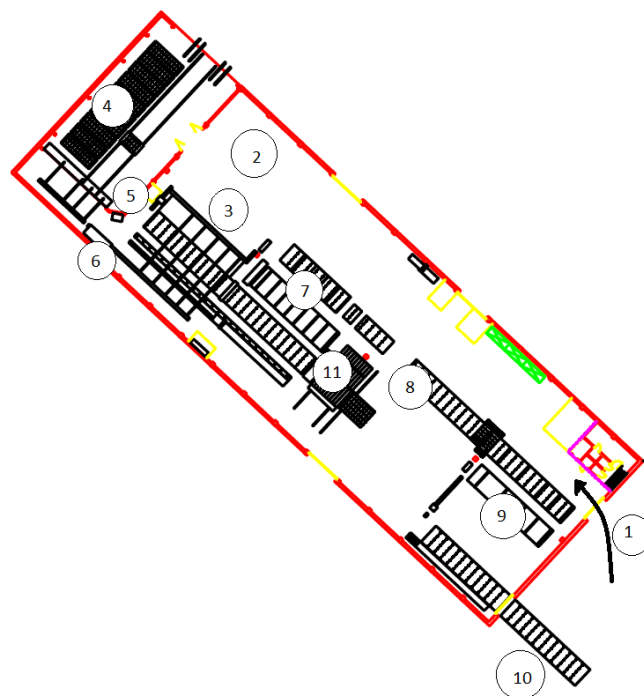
Layout för tillverkning och transport av halvfabrikat
